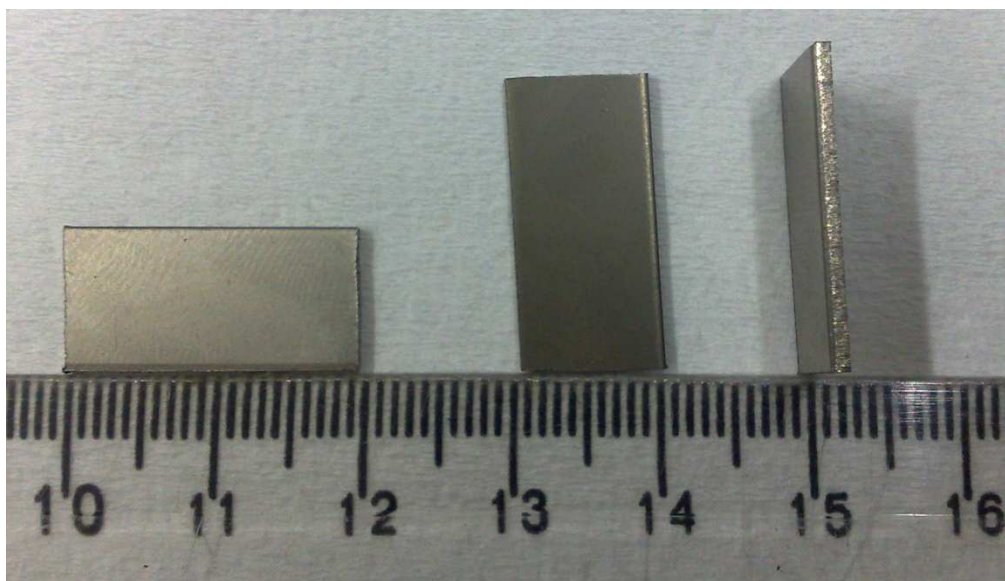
FOTO DAS CHAPAS ORIGINAIS DE Ti GRAU 2
